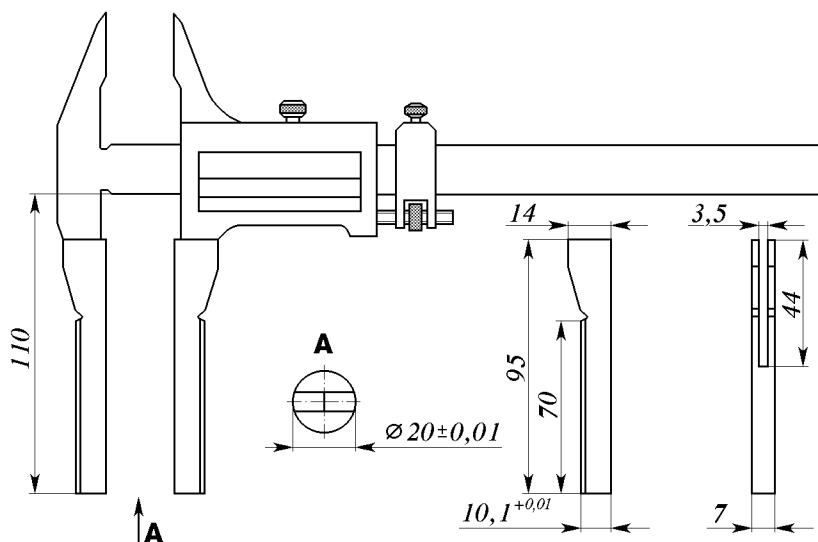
Штангенциркуль для замера натяга манжеты цилиндра подвески
